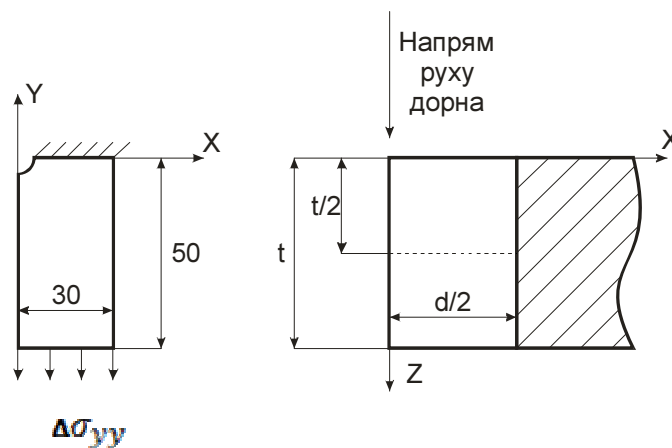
Схематичне креслення чверті робочої ділянки зразка
